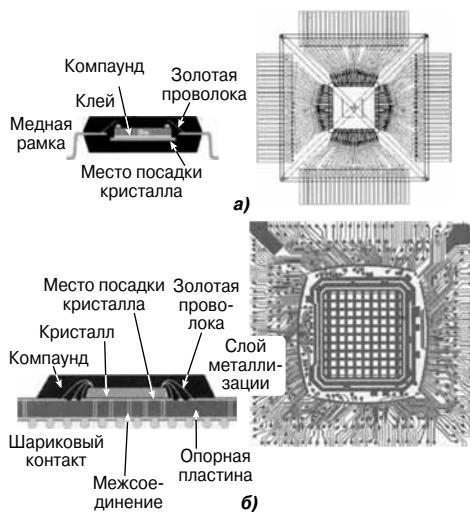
Вид сверху и изображение в поперечном разрезе корпусов с выводной рамкой (а) и типа BGA (б).
